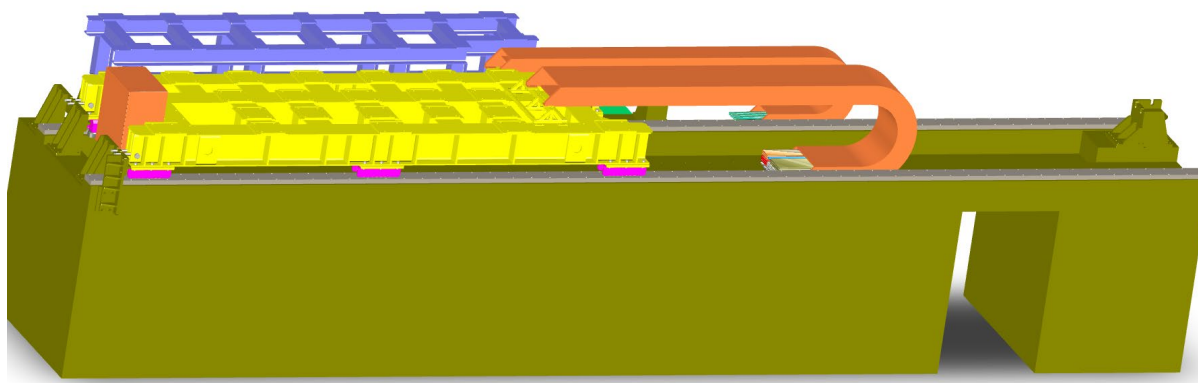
Общий вид платформы MUCH в рабочем положении
